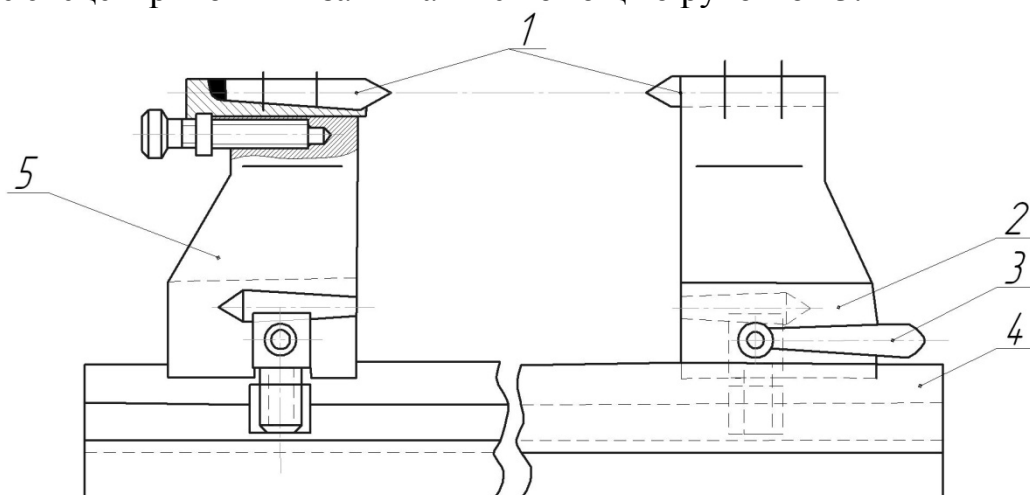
Приспособление для плоского шлифования цилиндрических заготовок в центрах
